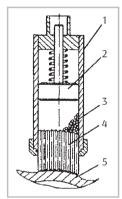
Схема шарикостержневого упрочнителя: 1 — корпус; 2 боек; 3 – стальные шарики; 4 — стержни; 5 — обрабатываемая поверхность
